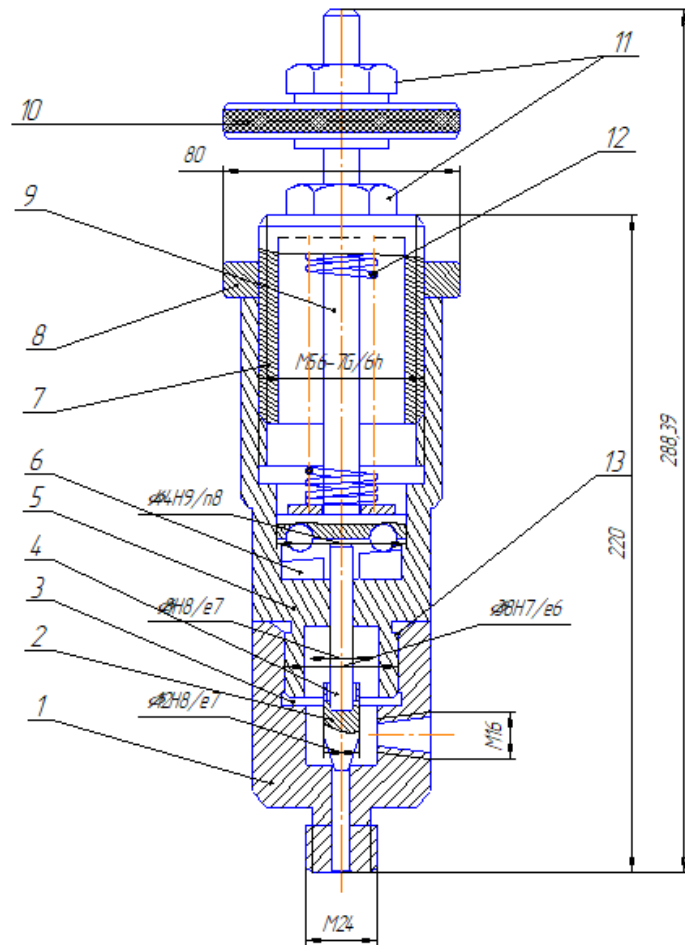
Будова проміжного клапана: 1 – установча втулка; 2 – клапан; 3 – тарілка клапана; 4 – штовхач; 5 – корпус; 6 – тарілка пружинна; 7 – пробка; 8 – планка; 9 – вісь; 10 – комірць; 11 – гайки; 12 – пружина; 13 – манжета.
